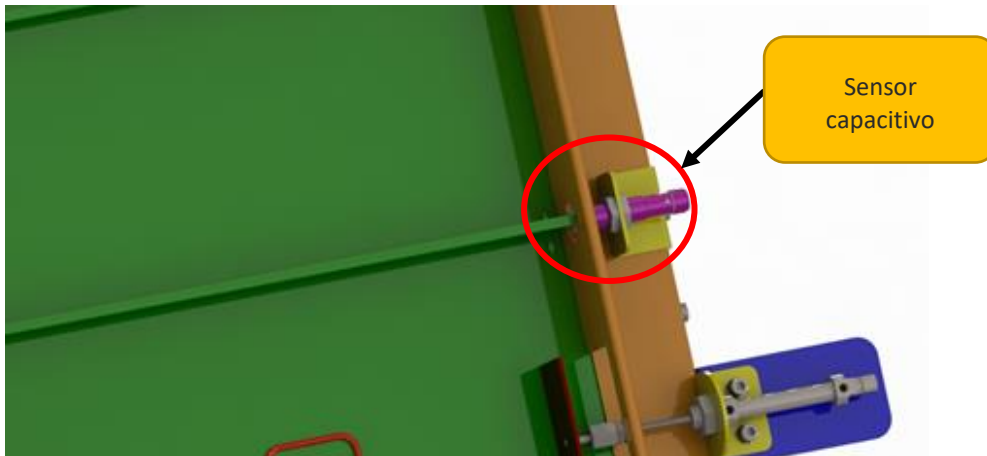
Sensor capacitivo a “ler” perfil de PVC
